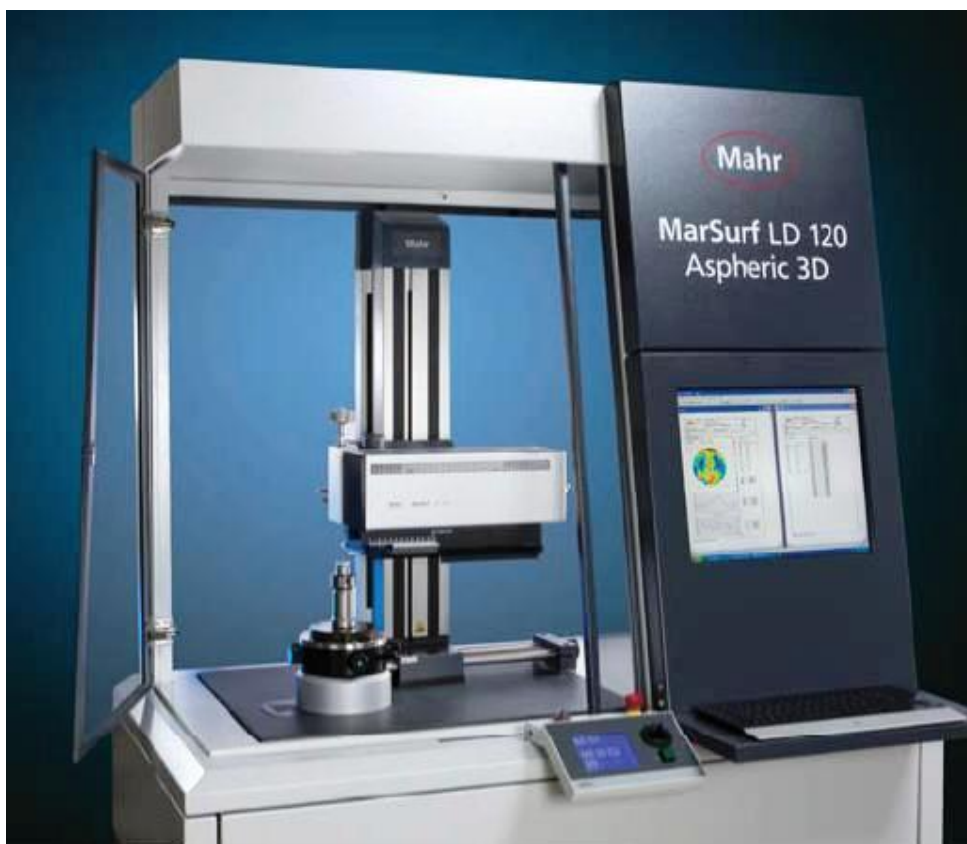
Общий вид прибора MarSurf LD 120 Aspheric 3D с приспособлением для крепления асферических деталей и устройством перемещения колонны по оси X.
